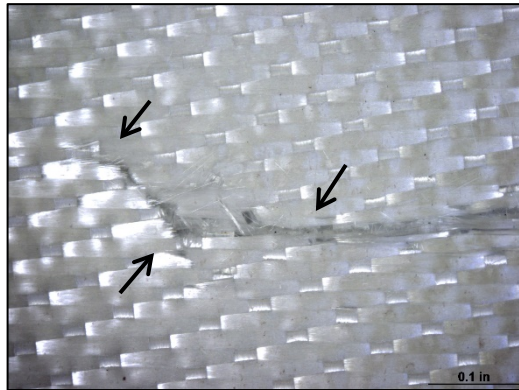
Zona de fractura de probeta 3 de 3 capas. Flechas indicando daño de fibras por sometimiento a prueba de impacto.
